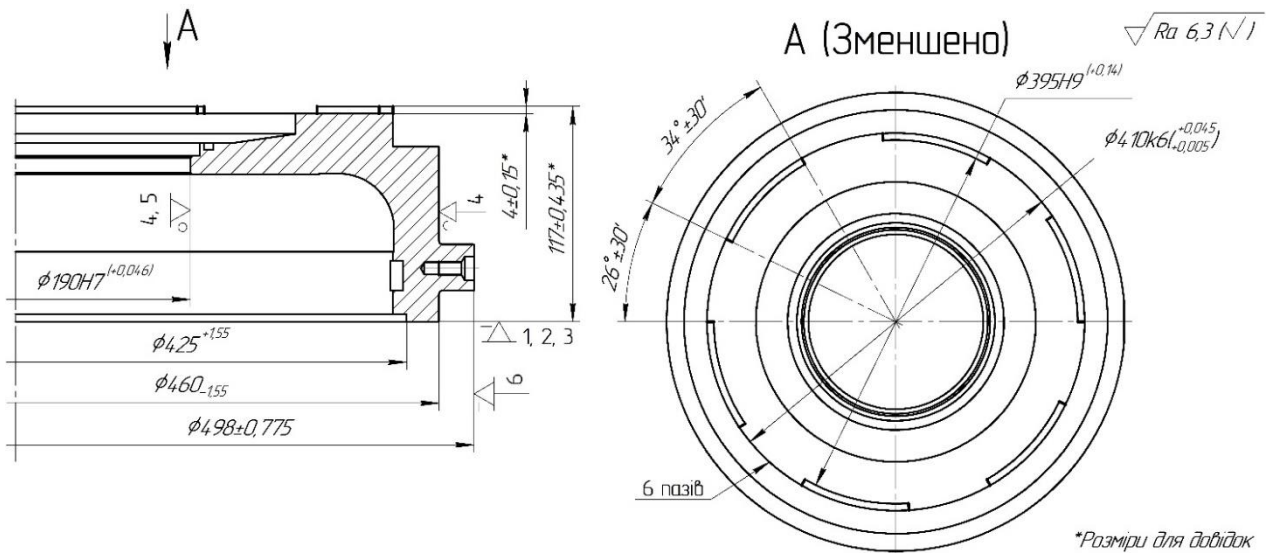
Ескіз заготовки на операції 035. Установ Б
